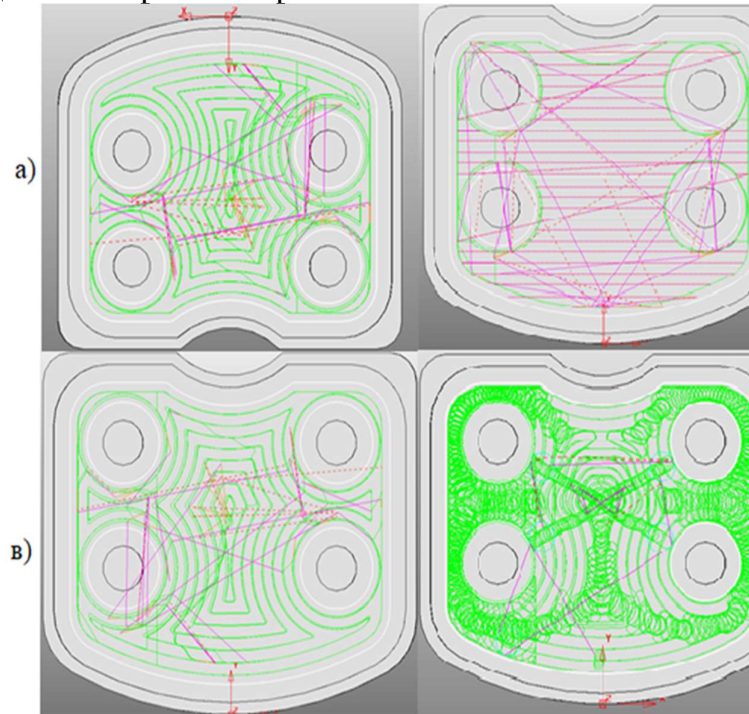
Траєкторії обробки робочої поверхні прес-форми:
